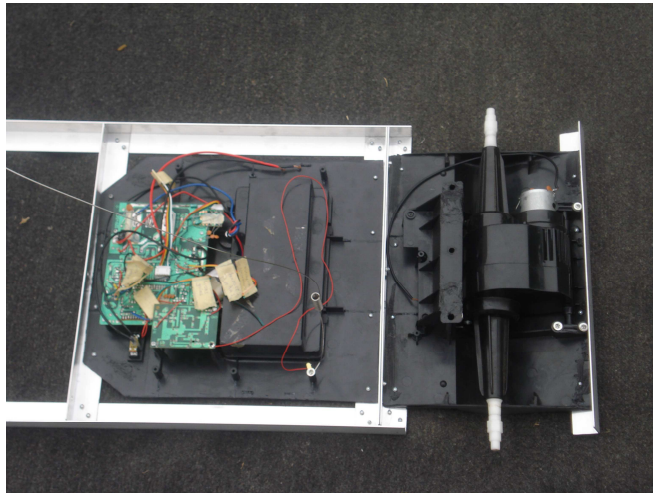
Ensamblaje de la placa de soporte y transmisión.
